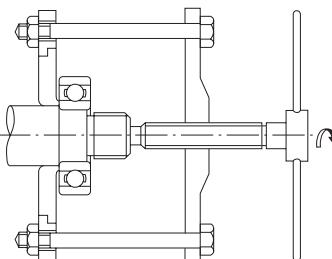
Demontage des Innenrings mit Abziehwerkzeug (1)
